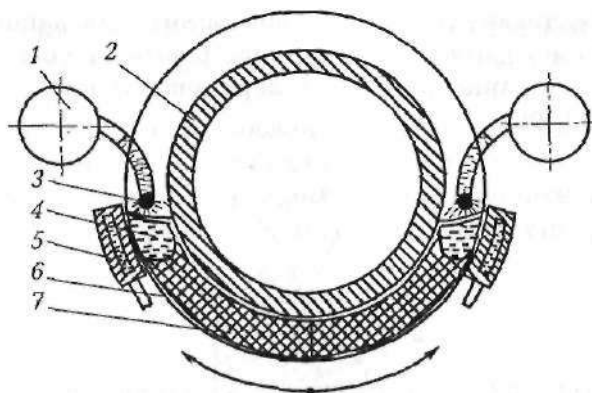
Схема процесса сварки труб больших диаметров порошковой проволокой с принудительным формированием шва:
